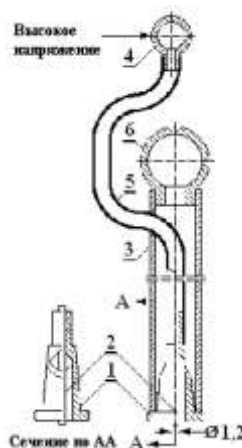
Одноструйный полиэтиленовый капилляр со сменной конусной головкой
